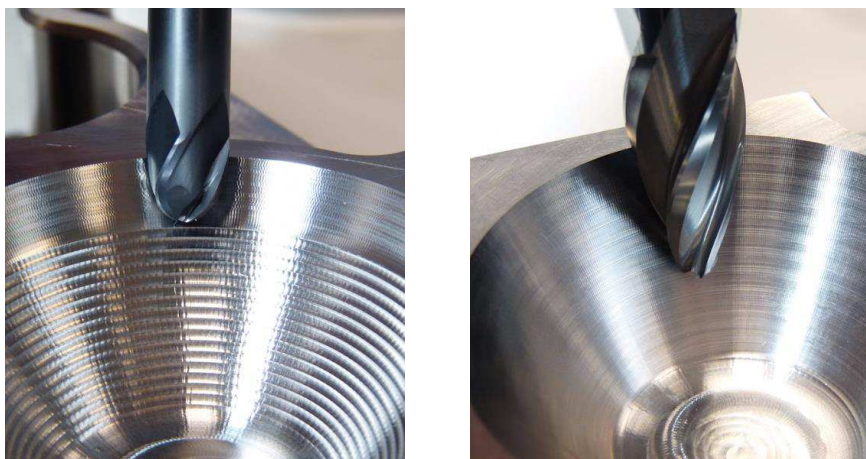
Rozdílná hodnota  $a_p$  pro soudečkovou frézu (nalevo) a kulovou frézu [67].
